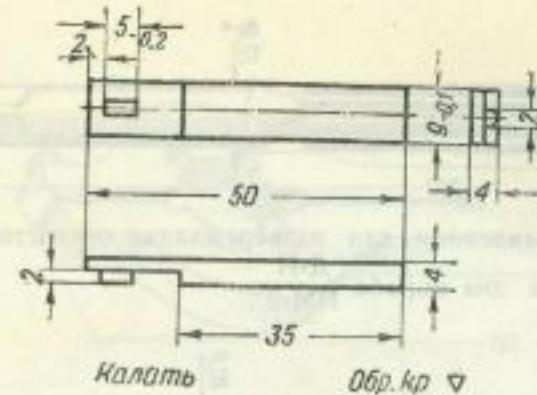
Оправка для выступа пружины крышки маслёнки затыльника. Ст. У8, ГОСТ В-1435-42.
